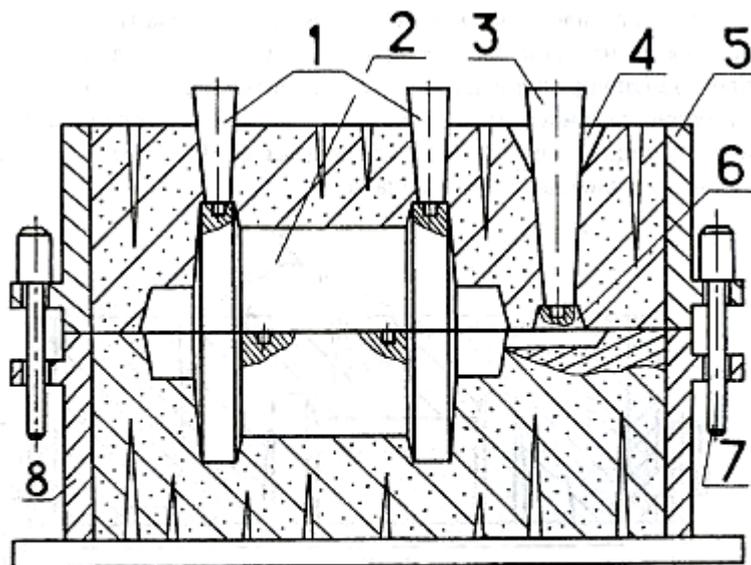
Набитые верхняя и нижняя опоки - полуформы: 1 - модели выпоров; 2 - модель отливки; 3 - модель стояка; 4 - литниковая чаша; 5 - верхняя опока; 6 - модель шлакоуловителя; 7 - центрирующий штырь; 8 - нижняя опока
